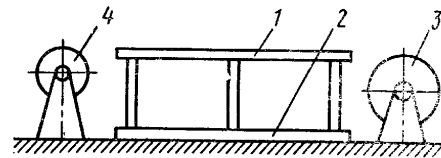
Схема установки для сборки и сварки полотнищ
